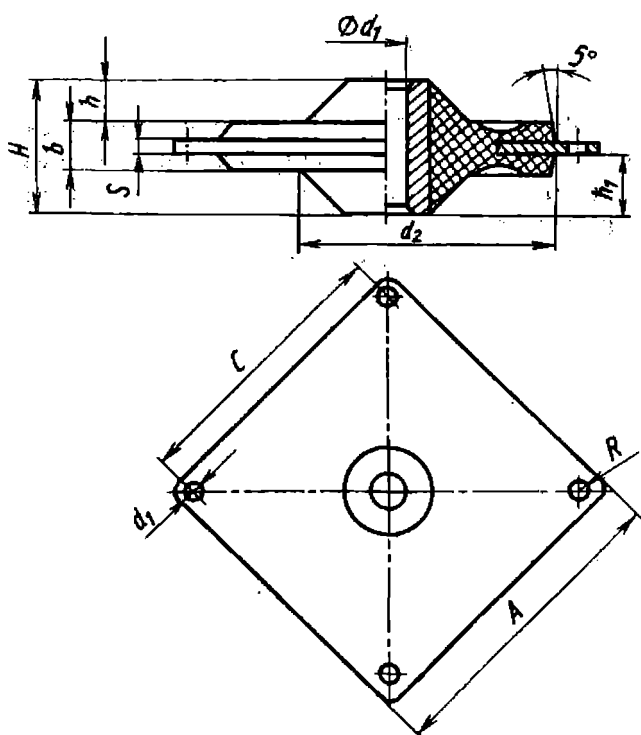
Конструктивные размеры и основные показатели виброизоляторов типа АП с квадратной пластиной из стали
